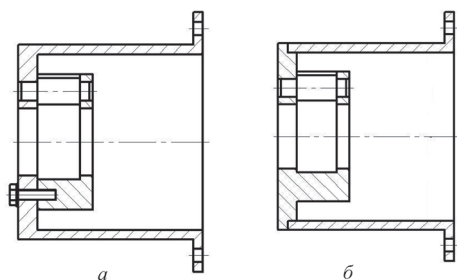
Варианты конструкций кожуха корпуса водила: а – отлитый из чугуна, соединенный болтами с водилом; б – полученный горячей штамповкой и стальной толстостенной трубы
